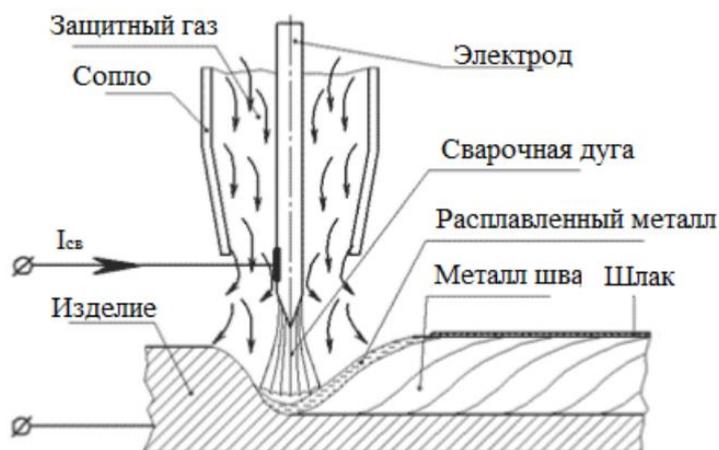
Схема сварки в среде защитных газов неплавящимся электродом
